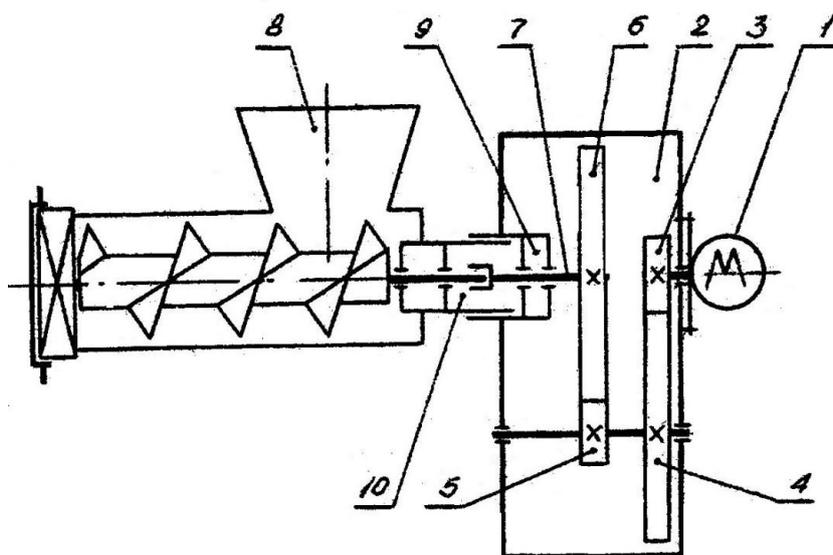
Схема привода ПМ-11 с мясорубкой МС2-150
